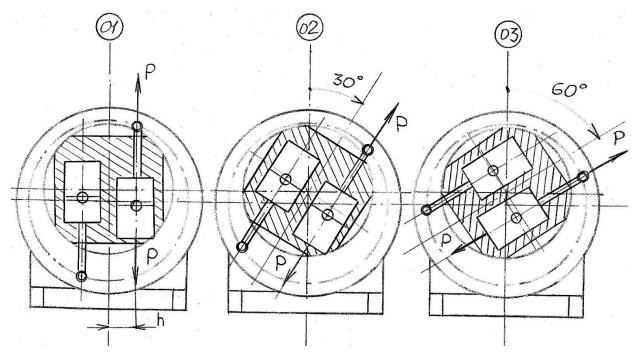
Чертёж позиций поршней и цилиндров роторного двигателя в процессе вращения
